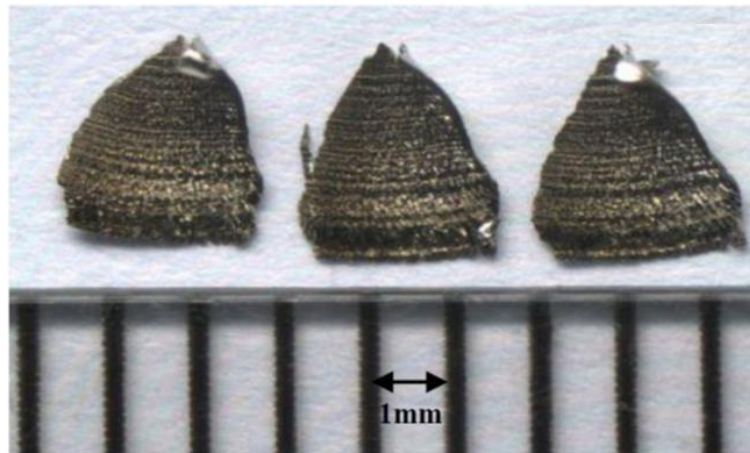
Cavaco descontínuo obtido por usinagem de material Inconel 718, com fresa de topo esférico em estratégia de corte concordante [21]
